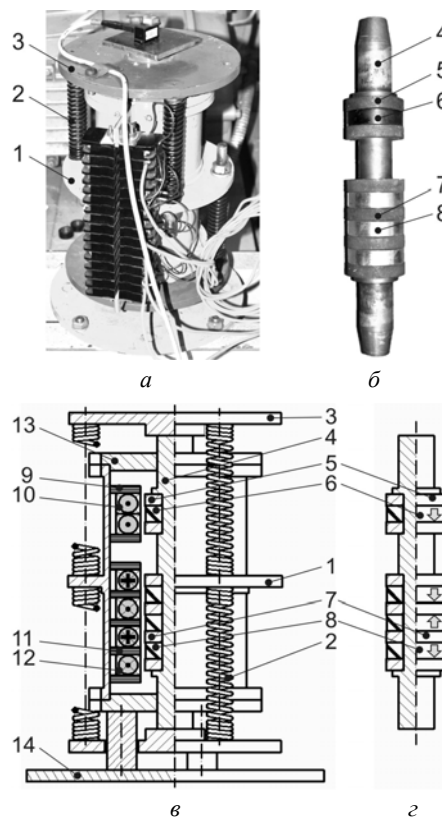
Коаксиально-линейный двигатель с магнитной пружиной: а – внешний вид КЛД-МП; б – внешний вид бегуна КЛД-МП; в – конструкция КЛД-МП; г – конструкция бегуна КЛД-МП
